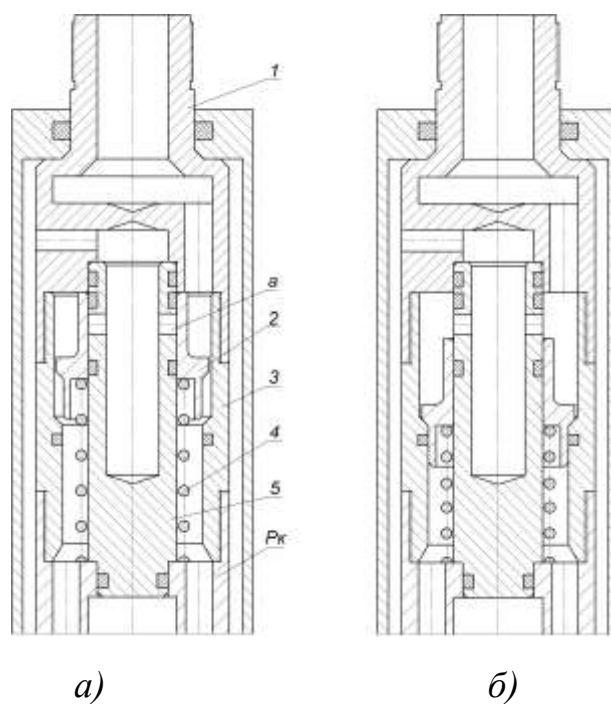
Схема ВРУ с клапанно-золотниковым распределительным узлом: 1 – переходник; 2 – клапан; 3 – корпус; 4 – пружина; 5 – шток; Рк – распределительная коробка гидроударника
